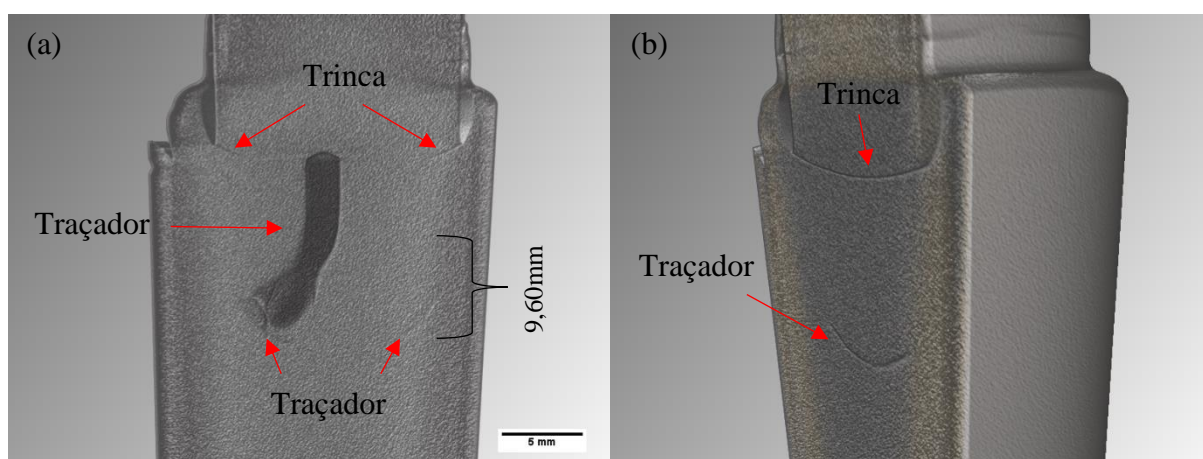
Vista da seção transversal no centro da junta soldada (a) e vista da seção transversal deslocada do centro da junta soldada (b) da amostra 08.
